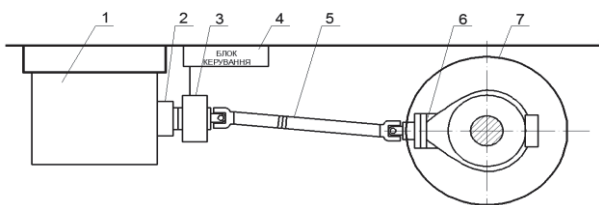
Принципова схема місця розміщення електромагнітного вихорострумового обертового сповільнювача: 1 – підвагонний генератор, 2 – гумометалічна муфта, 3 – магнетардер, 4 – блок керування, 5 – карданний вал, 6 – редуктор, 7 – колісна пара
